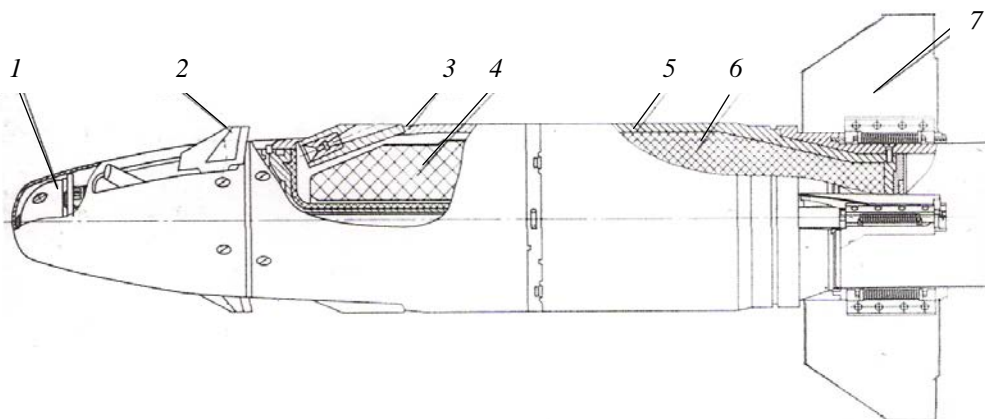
Конструктивная схема ракеты 9М119М: 1 – лидирующий предзаряд; 2 – руль; 3 – корпус; 4 – заряд маршевый; 5 – корпус; 6 – основнойкумулятивный заряд; 7 – лопасть
